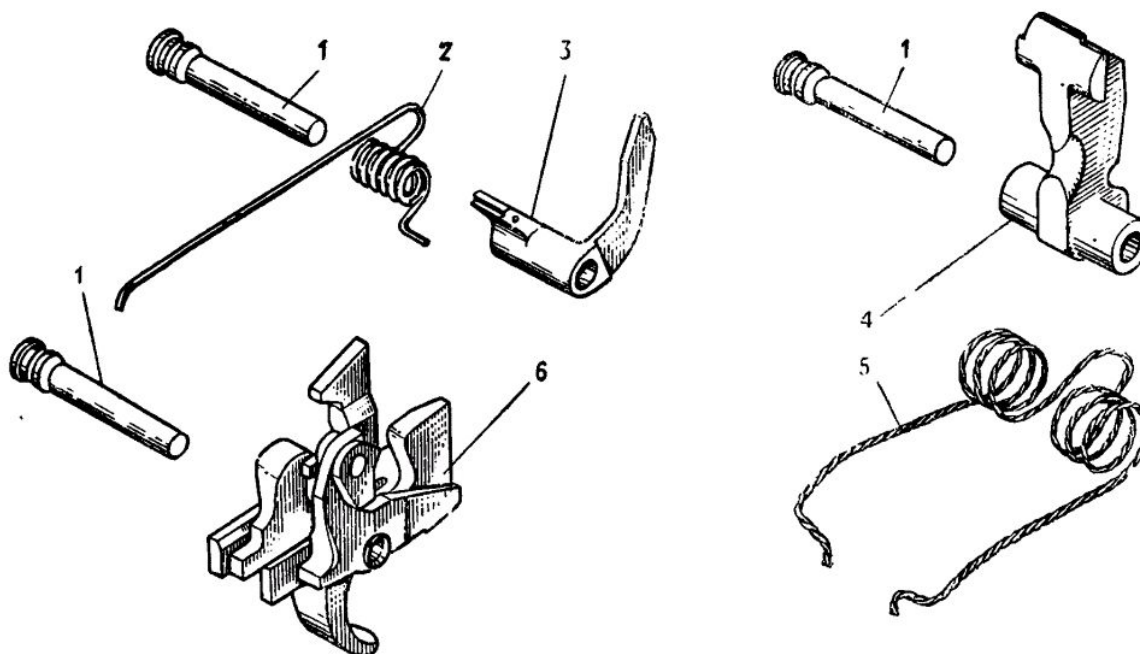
Детали и сборочные единицы ударно спускового механизма:
